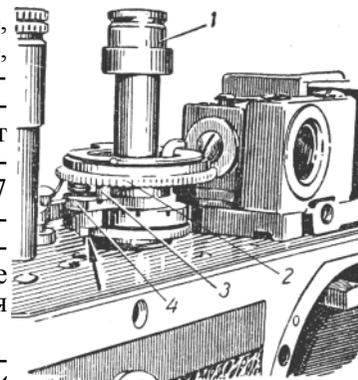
Расположение рычага экспозиции и пальца механизма замедления.
